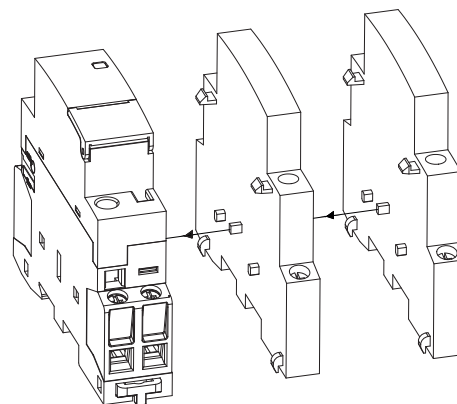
Блок-схема соединения контактора и дополнительных блоков / Figure 8 – Block diagram for connecting the contactor and auxiliary units
